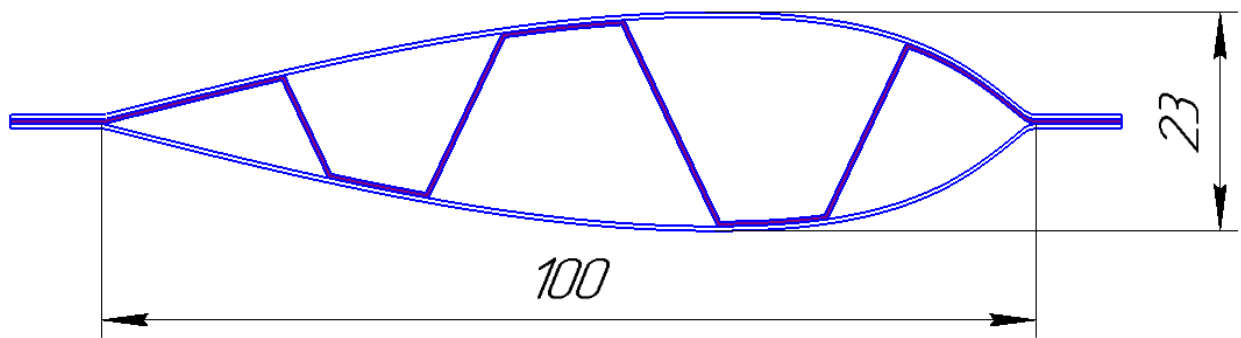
Поперечний переріз фрагменту металевої порожнистої лопатки
